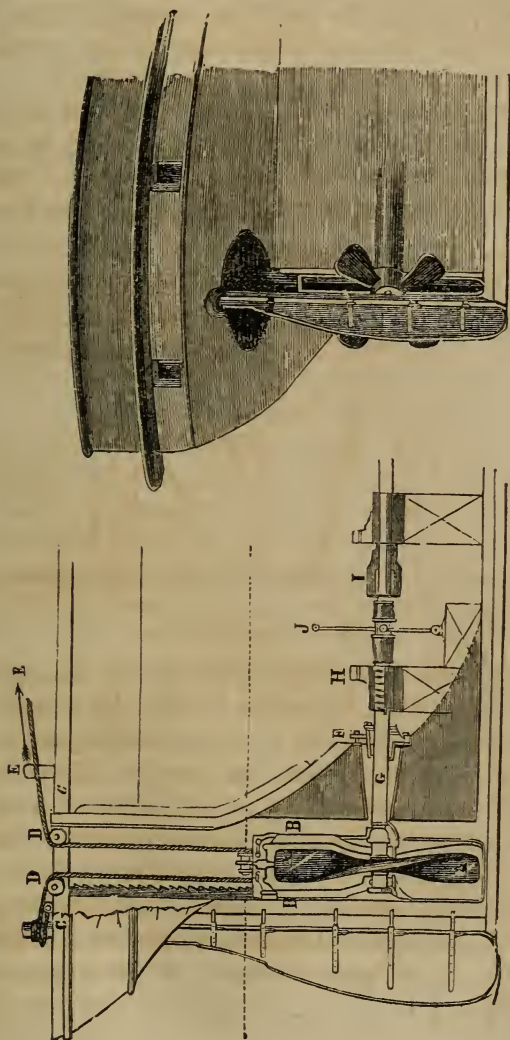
IL POZZO DELL'ELICE (sezione e prospetto).
